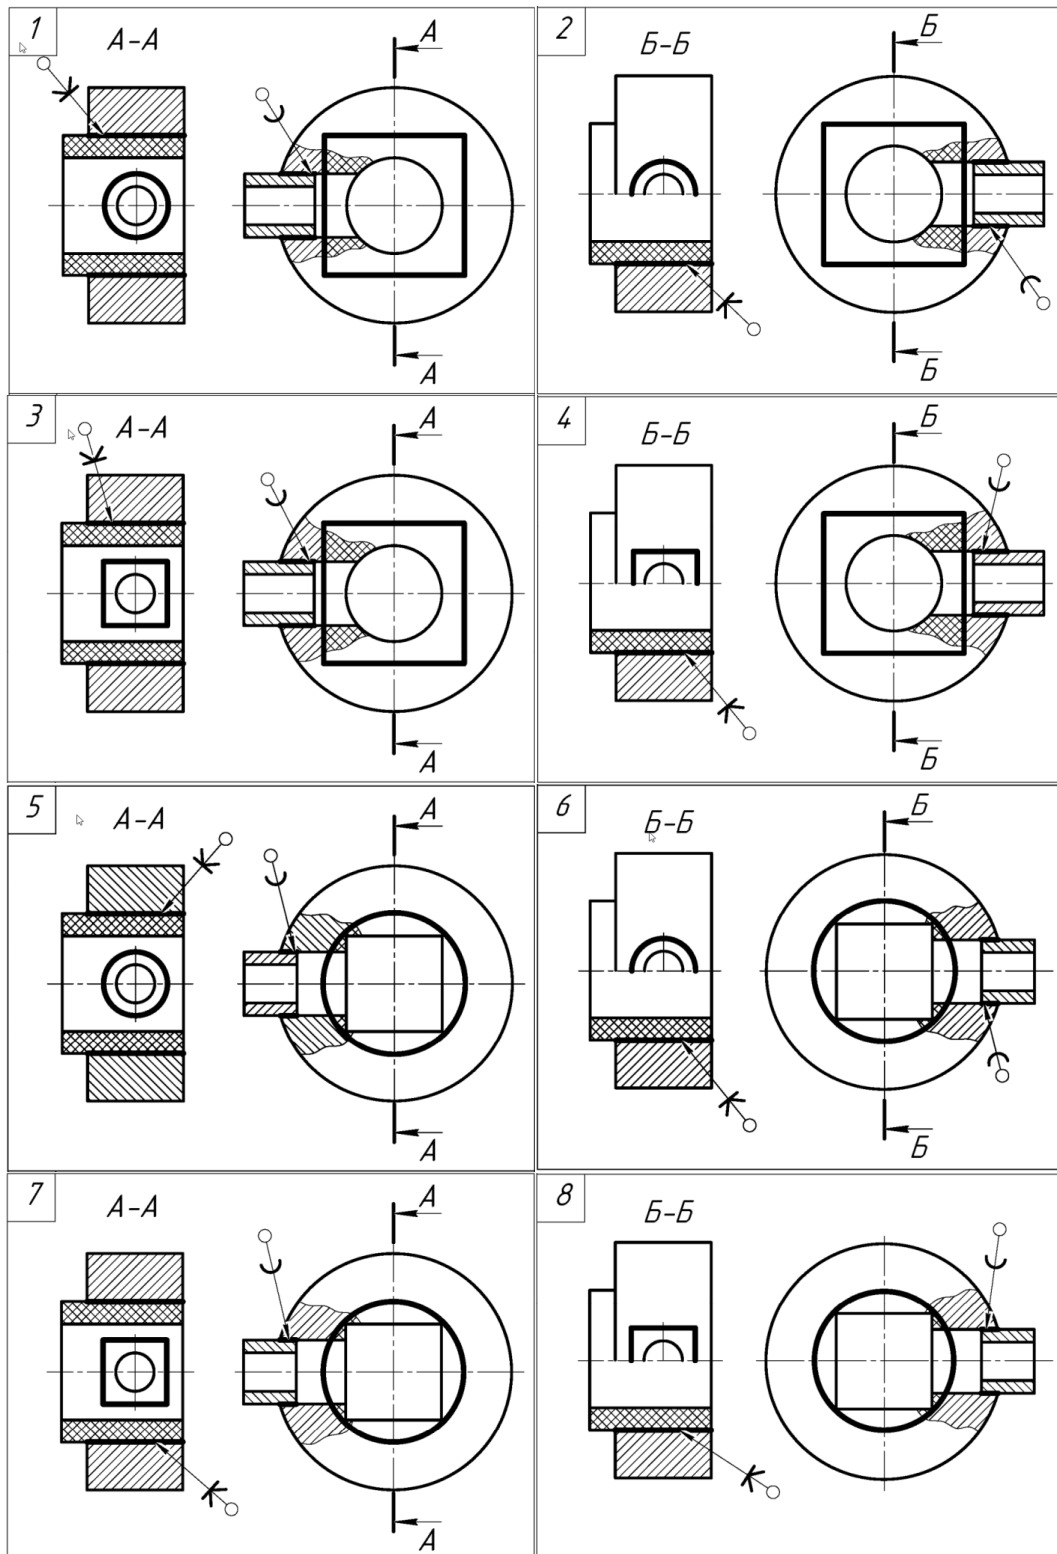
Сборочный чертеж соединение пайкой и клейкой
